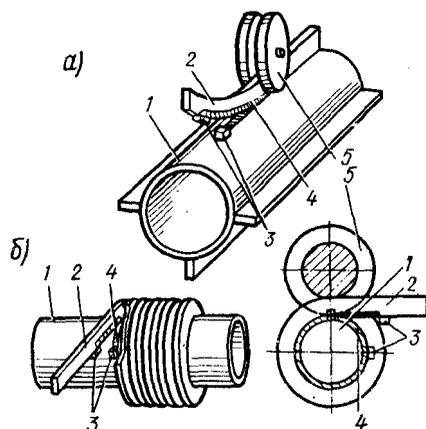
Приварка ребер к трубам с помощью контактной сварки ТВЧ:
